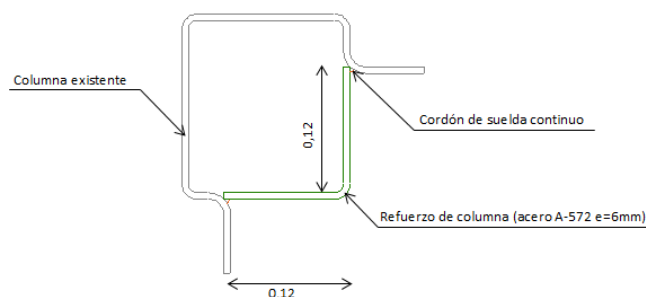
Detalle de refuerzo de Parante delantero de Contenedor
